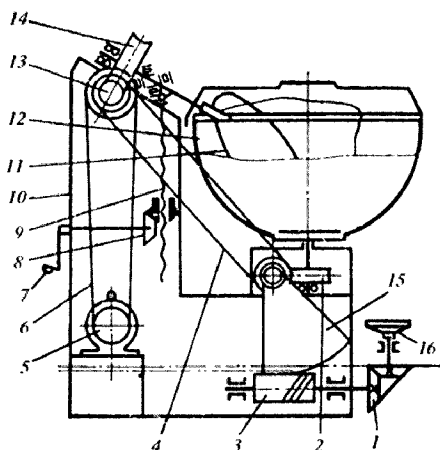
Кинематическая схема смесителя модели МЛ-100:
